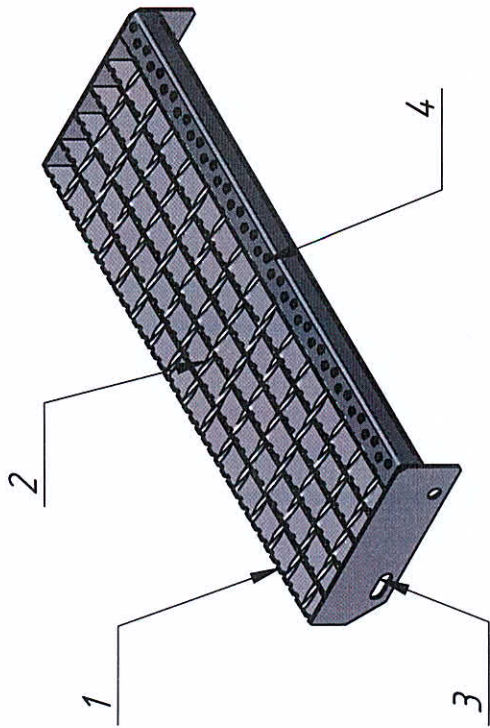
Ступень из сварного решетчатого настила
